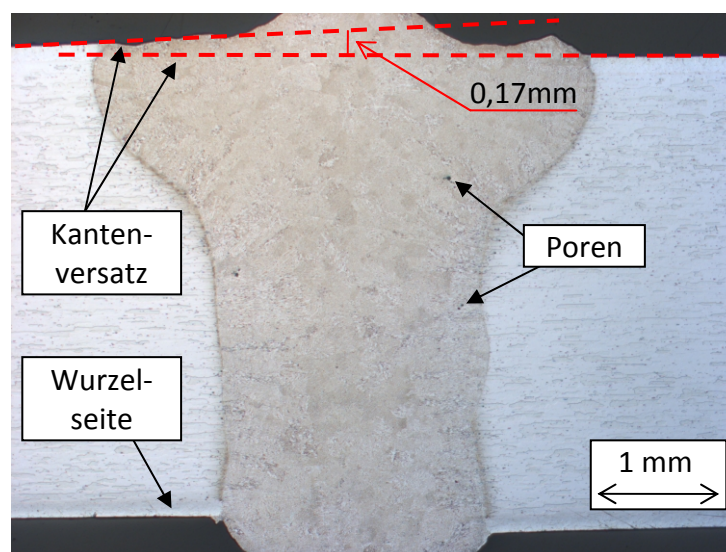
Querschliff einer Schweißnaht (EN AW-6156-T4 mit AlSi12)
